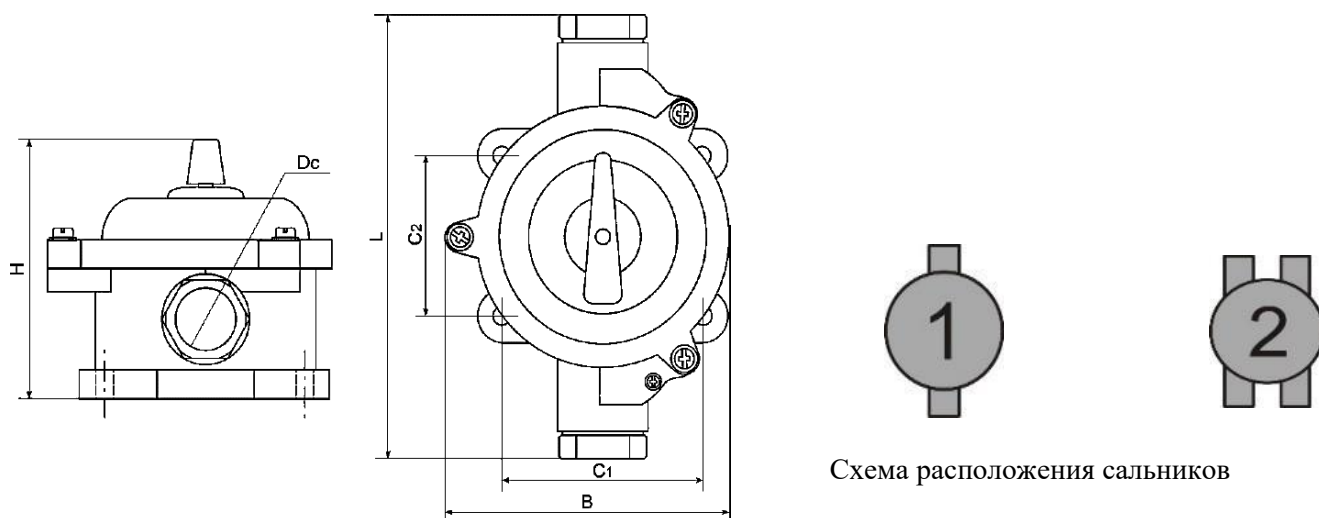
Габаритные и установочные размеры пакетных переключателей ПП. Исполнение в силуминовом корпусе. Степень защиты IP56. Способ крепления - основанием корпуса.
